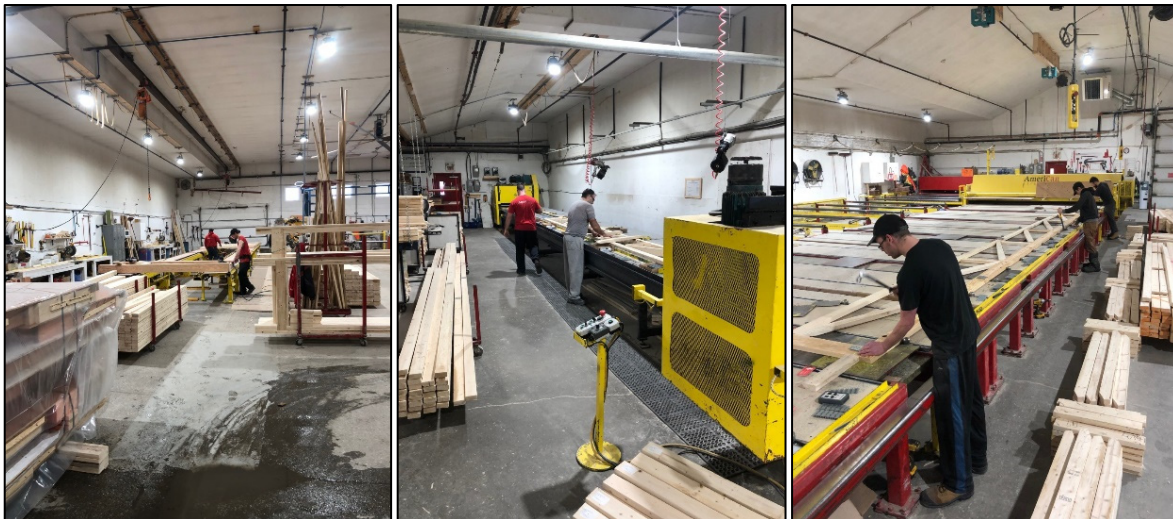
Section murs, fermes et poutrelles (de gauche à droite)
